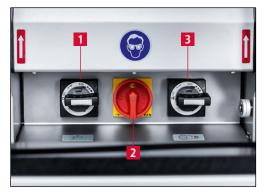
Schleifmaschine und Kühlmitteleinrichtung einschalten
